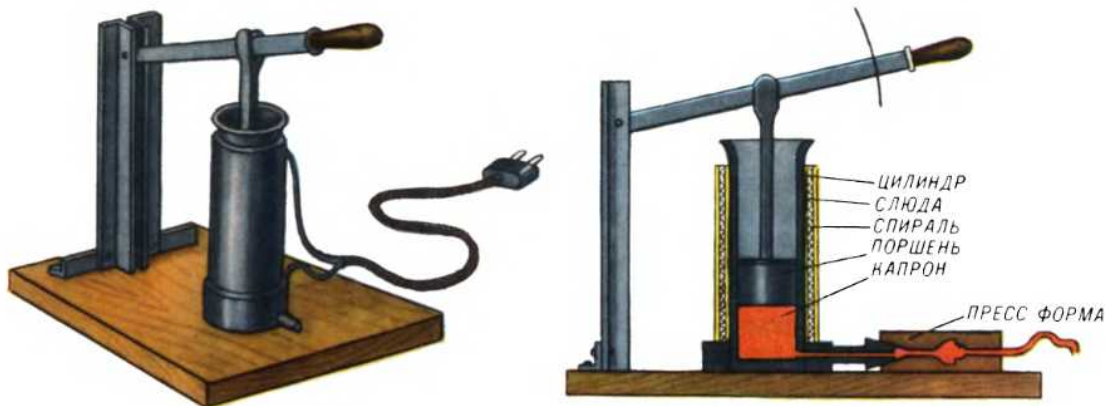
Приспособление для отливки мелких деталей под давлением из капрона и полистирола.
